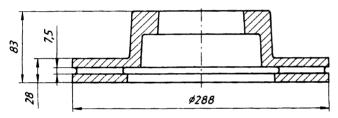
Чертеж отливки тормозного диска автомобиля "Газель"
